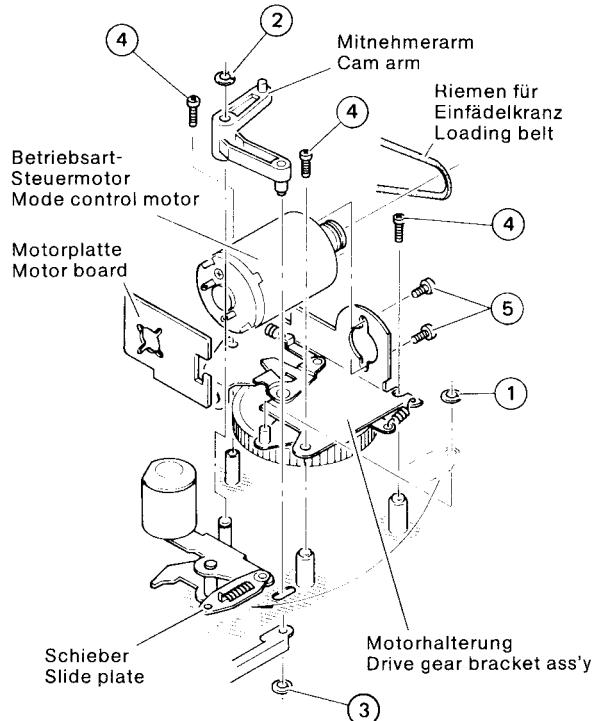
Ausbau des Betriebs-Steuermotors /
